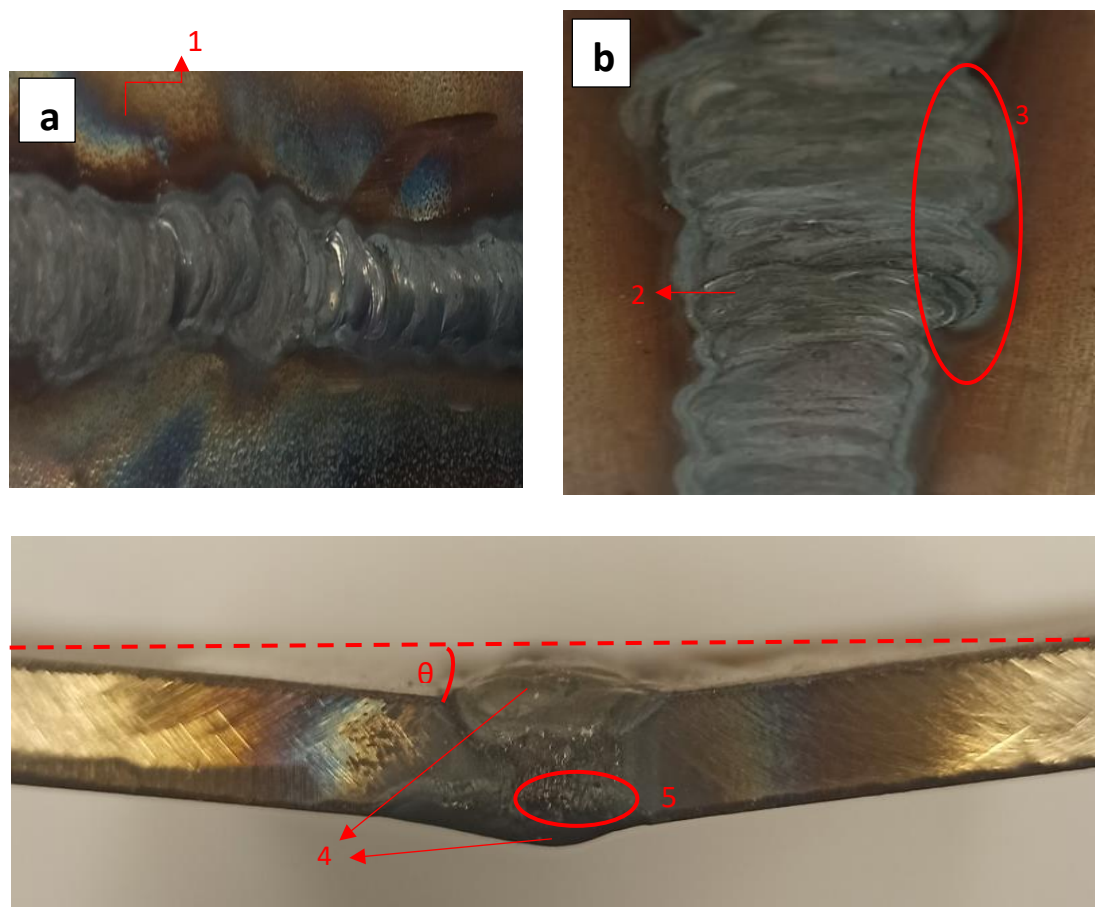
Piezas AISI 304L soldada por proceso TIG. a) Vista planta, b) Vista cara posterior y c) Vista alzada
